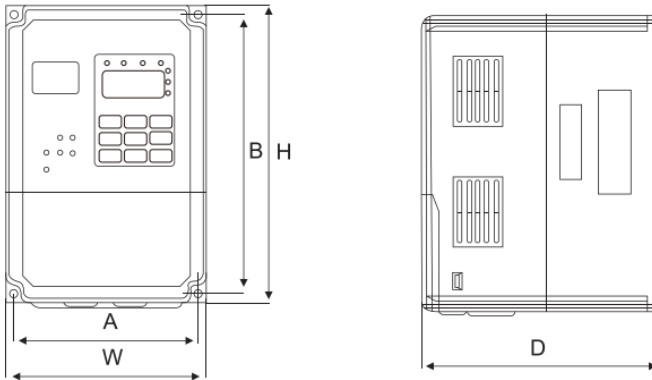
Внешний вид и размеры ПЧ (≤ 22 кВт)
